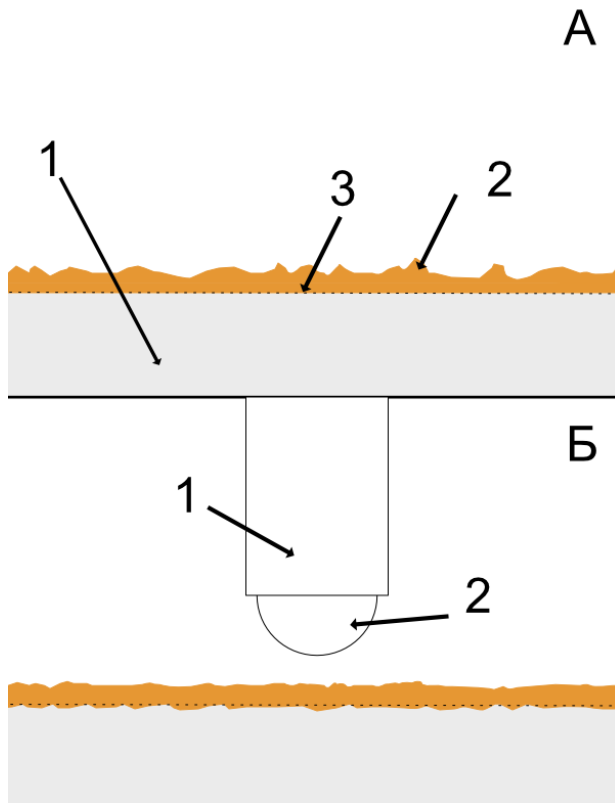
Схематическое представление обработки ультразвуком. А) 1-материал-подложка, 2-нанесённый материал покрытия, 3- линия разграничения двух материалов; Б) 1-ультразвуковой инструмент, 2-индентор из твёрдого сплава.
